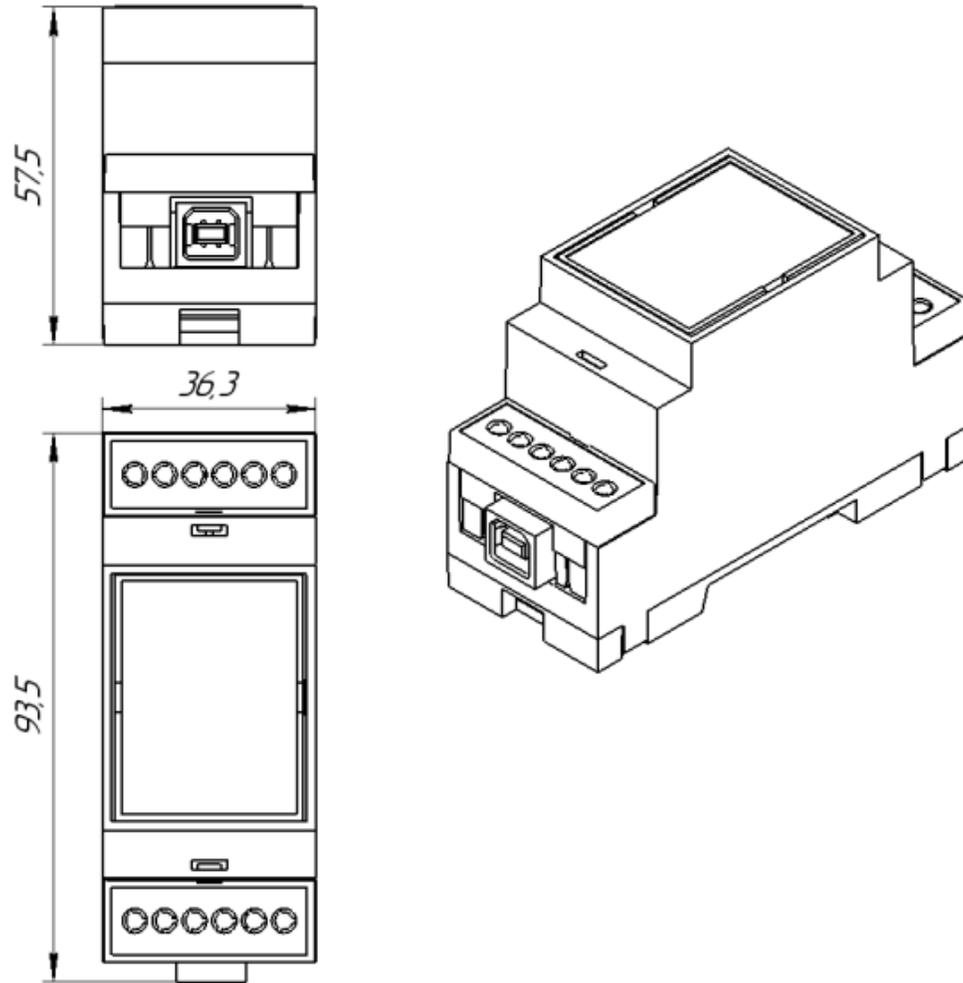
Габаритные размеры корпуса преобразователя интерфейсов
